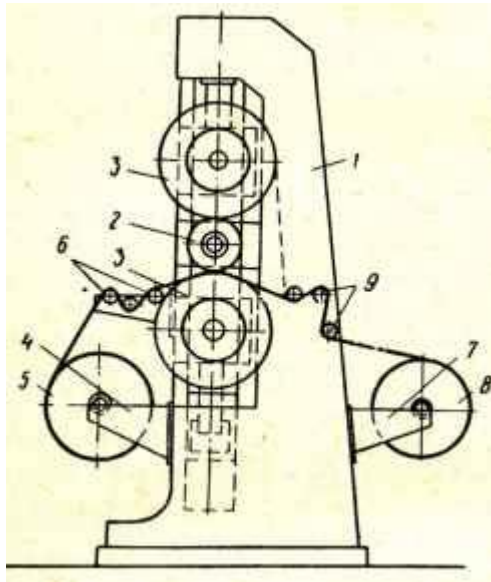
Схема будови трьохвального обробного каландра КО-3-120-1.
